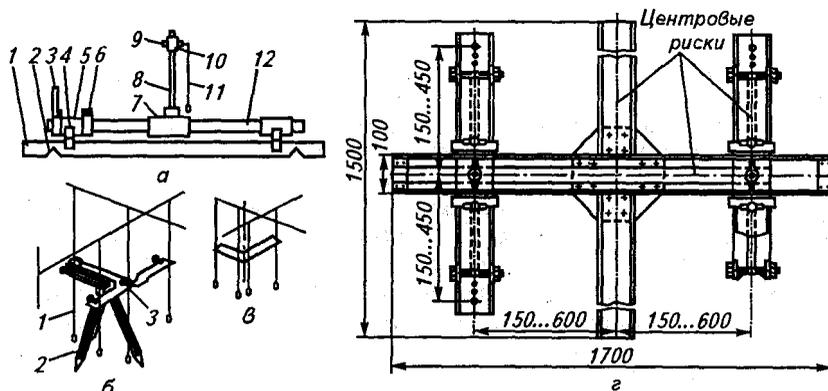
Универсальные приспособления для разметки линий, перпендикулярных или параллельных к заданной оси: а – поворотное: 1, 2 – основания; 3 – рукоятка; 4 – кронштейн; 5 – втулка; 6 – стопорный винт; 7 – тройник; 8 – штанга; 9 – разметочная игла; 10 – головка; 11 – отвес на нити; 12 – труба; б, в – для проведения перпендикулярных линий: 1 – отвес на нити; 2 – тренога; 3 – линейка; г – раздвижная линейка
